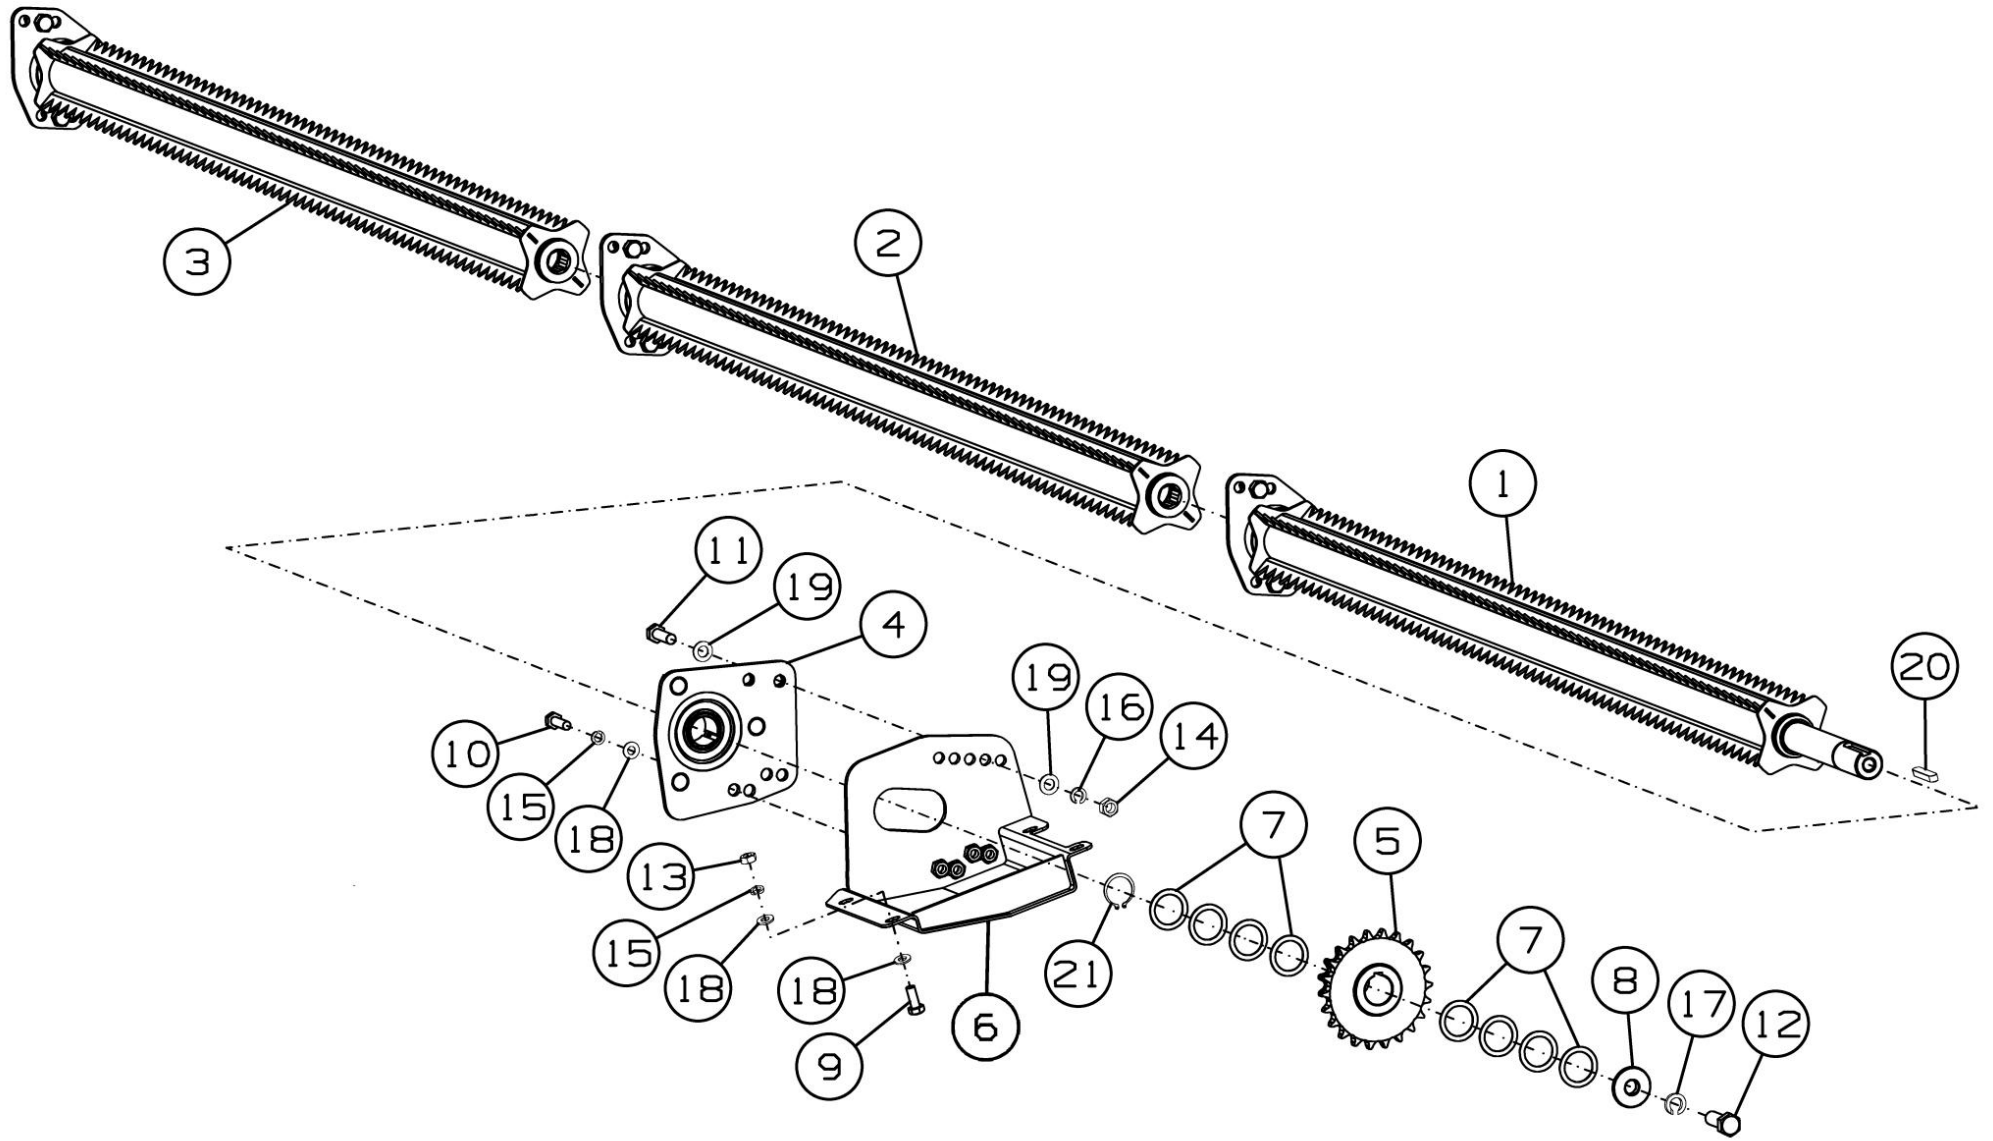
Вал протягивающий SS-780.01.06.000-03
